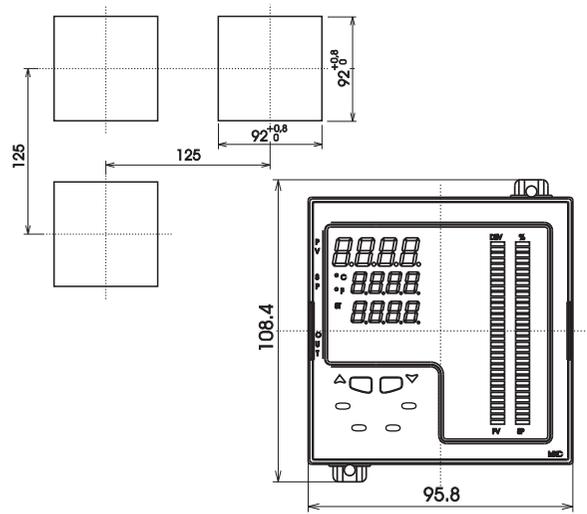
B DIMENSIONI E FORATURA PER MKP
